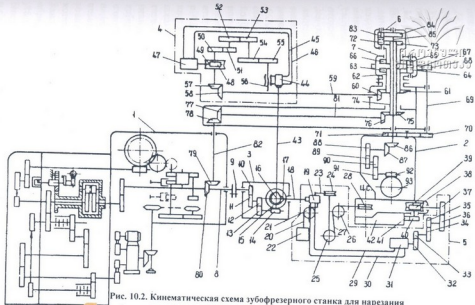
Кинематическая схема зубофрезерного станка для нарезания некруглых конических колес с круговыми зубьями
